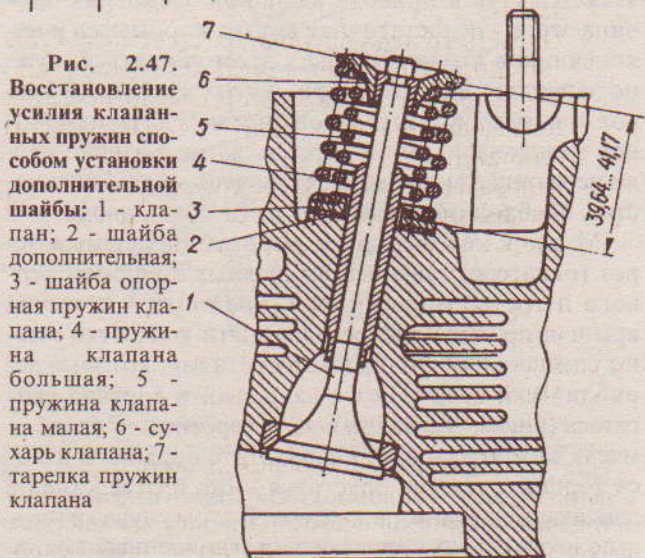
Восстановление усилия клапанных пружин способом установки дополнительной шайбы: 1 - клапан; 2 - шайба дополнительная; 3 - шайба опорная пружин клапана; 4 - пружина клапана большая; 5 - пружина клапана малая; 6 - сухарь клапана; 7 - тарелка пружин клапана
